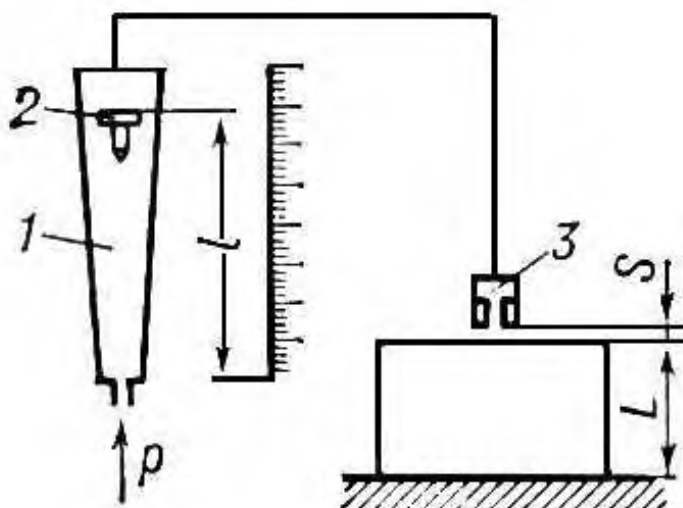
Пневматичний вимірювальний прилад ротаметричного типу:
